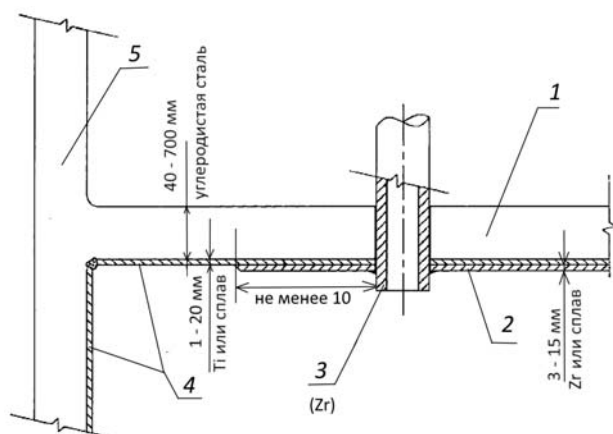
Внутреннее устройство кожухотрубного теплообменника для работы с агрессивными жидкостями: 1 – трубная решетка; 2 – накладка; 3 – труба; 4 – облицовка; 5 – стенка кожуха
